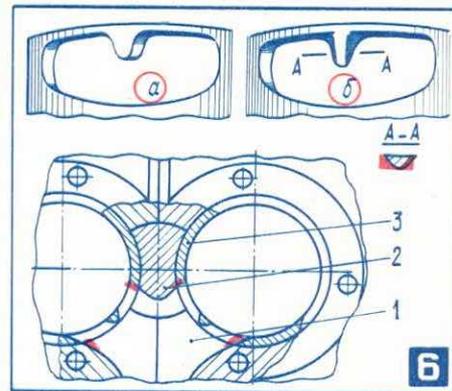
Обработка впускного канала на входе в цилиндр: а — стандартное исполнение; б — скругленные выступа; 1 — картер; 2 — вилдыш; 3 — цилиндр.
